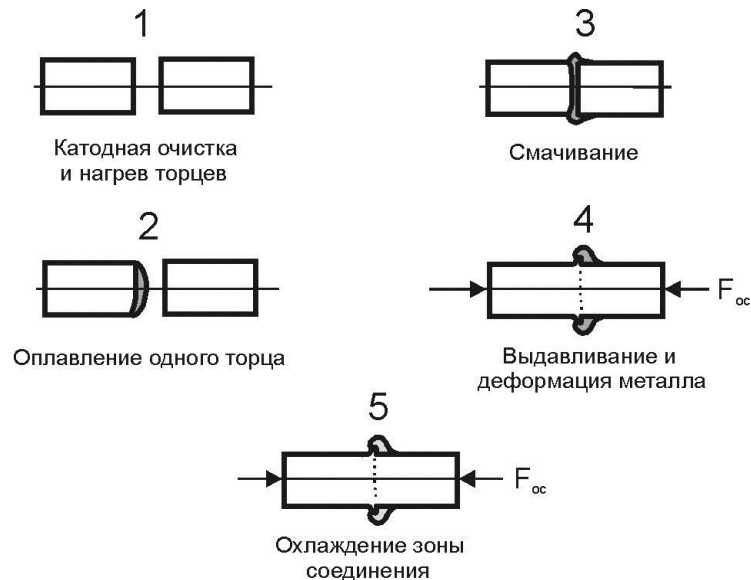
Схема формирования сварных соединений труб из разнородных металлов
